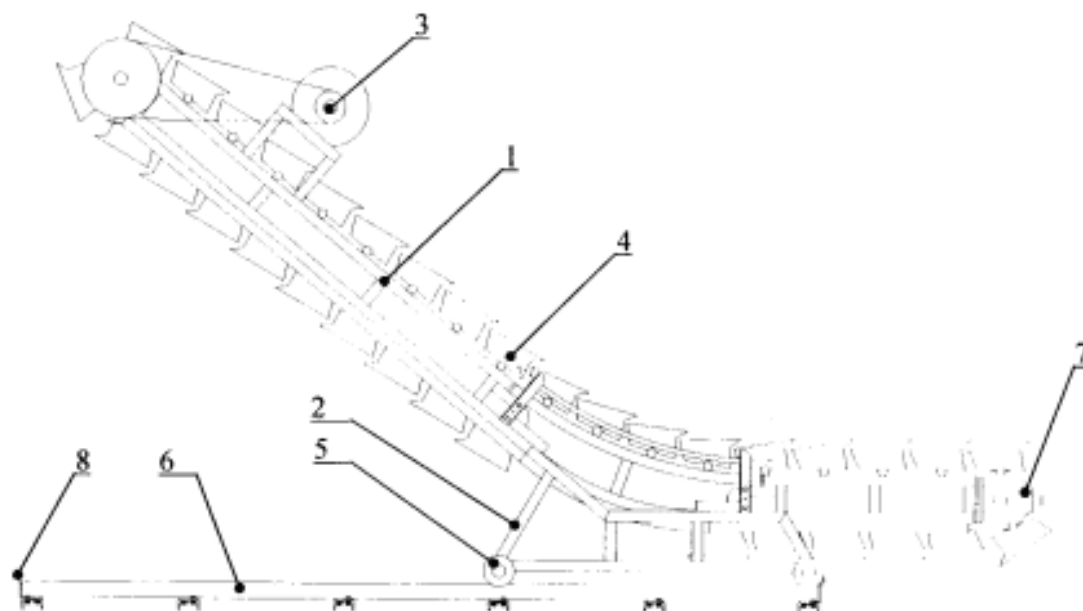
Элеватор ковшовый: 1 – рама; 2 – тележка; 3 – привод транспортера; 4 – ковши; 5 – катки; 6 – рельсовый путь; 7 – натяжное устройство; 8 – фиксаторы
